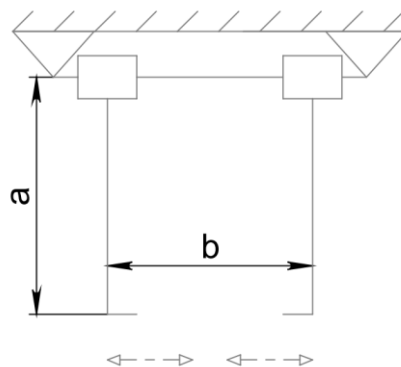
Кинематическая схема захвата с поступательным движением
